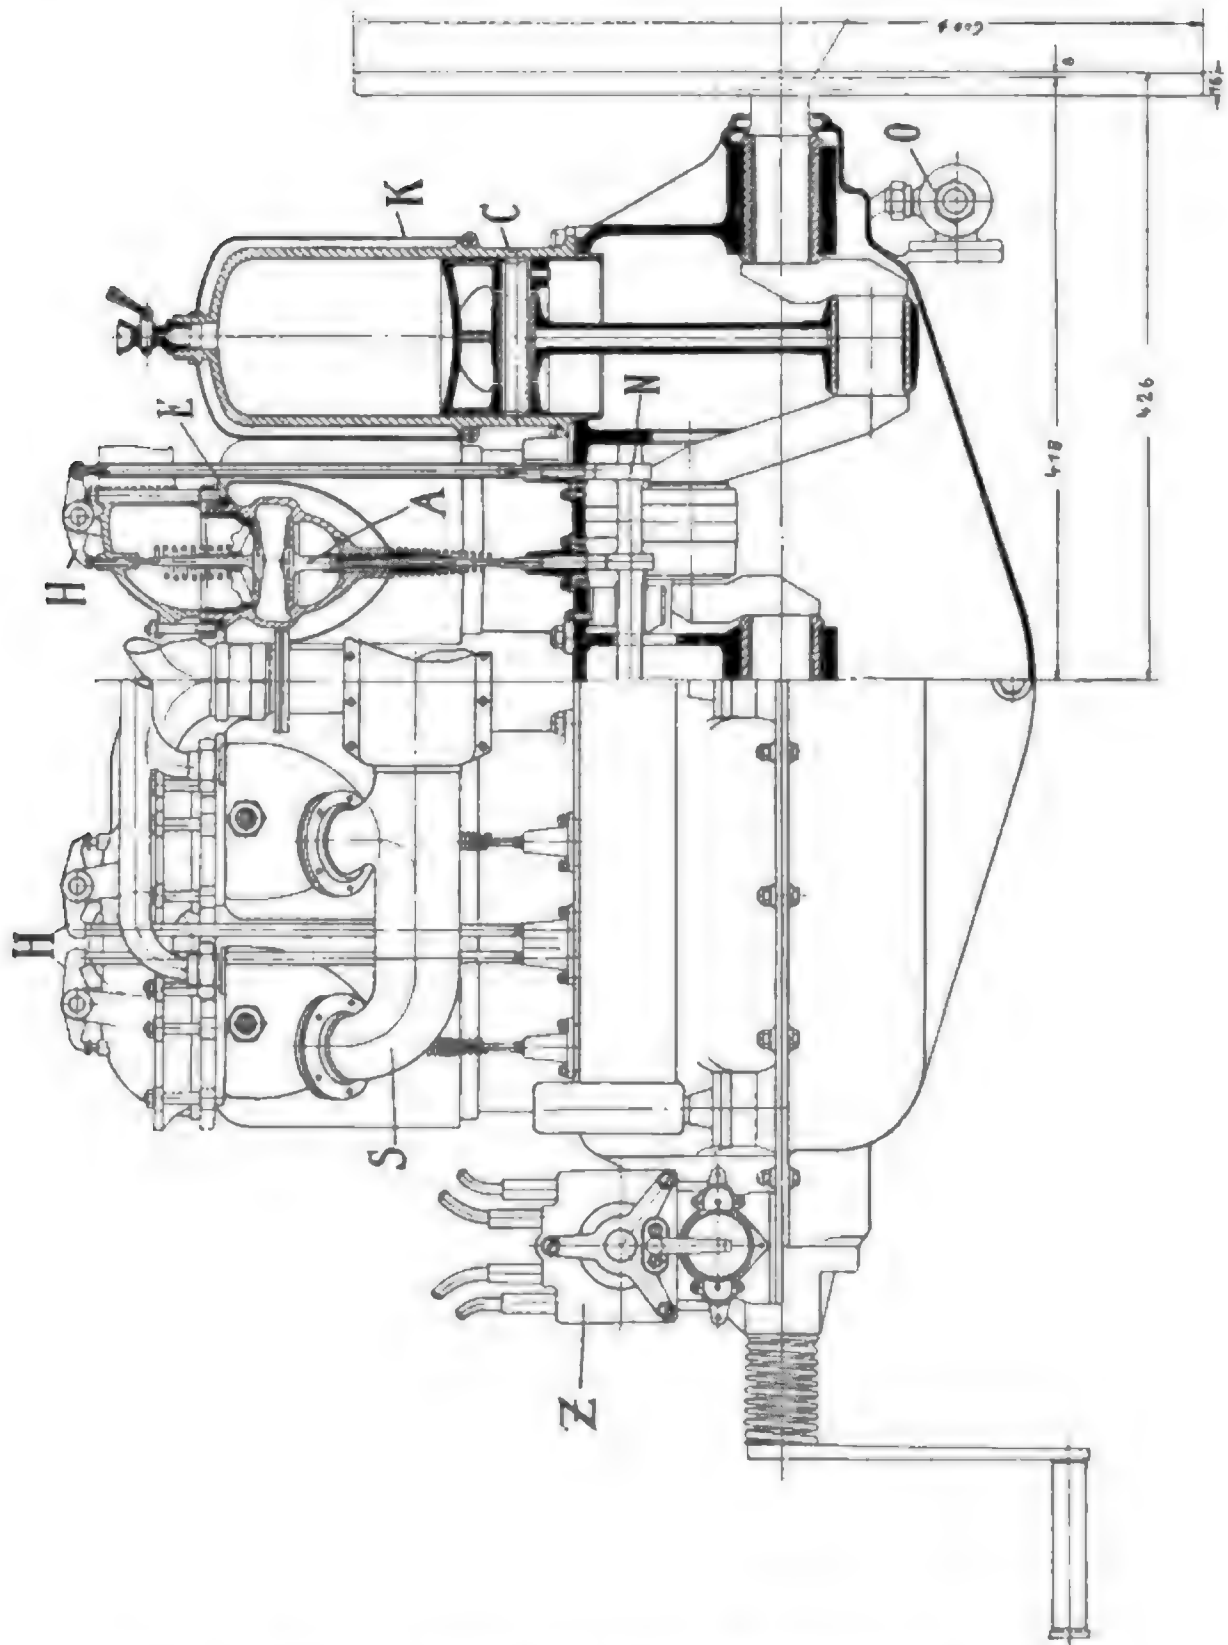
Zeichnung des Flugmotors von Körting, Seitenansicht bzw. Längsschnitt.
